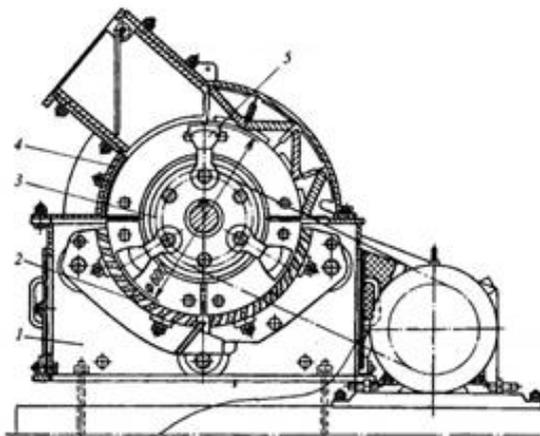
Молотковая дробилка: 1- станина; 2- колосниковая решетка; 3- ротор; 4 – корпус; 5 – молотки
